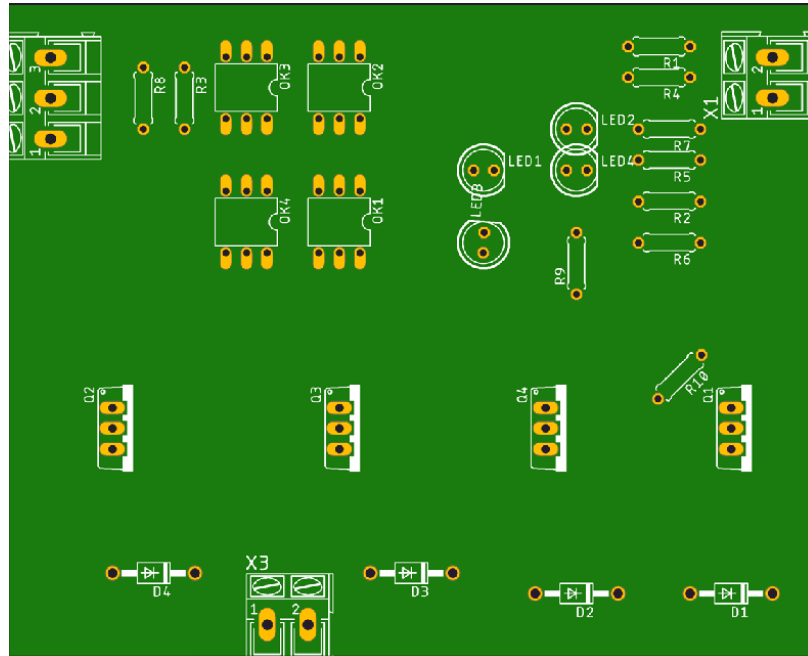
Vista superior del diagrama de la tarjeta PCB (vista 1)
